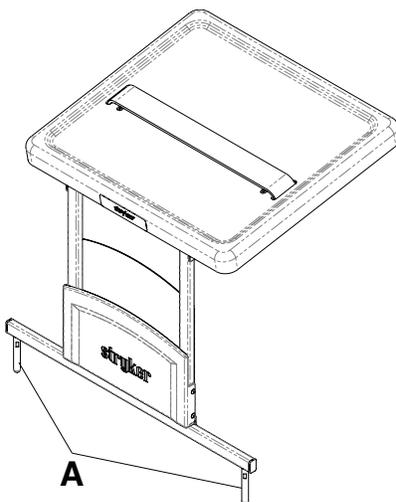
Присоединение лотка для дефибриллятора/держателя планшета
